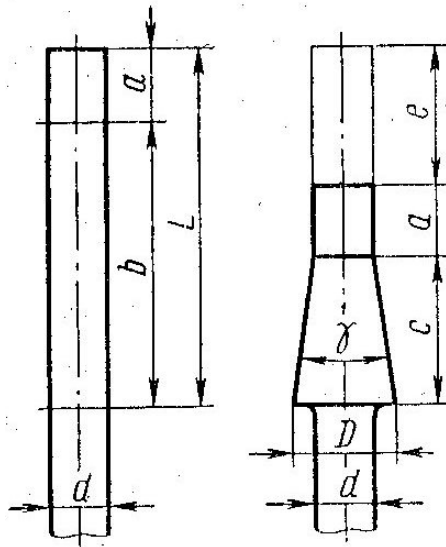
Заготовка вихідна і після висадки в пуансоні з конічною порожниною.
